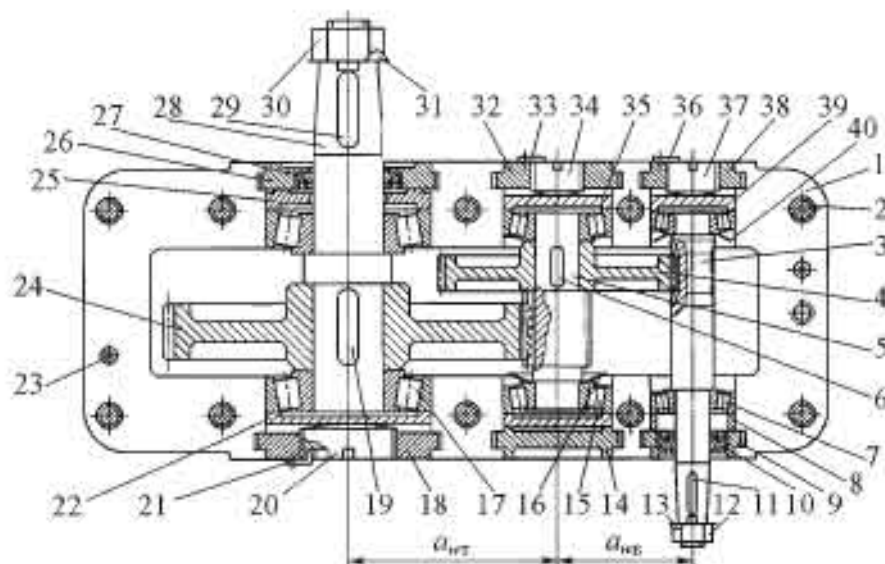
Конструкция двухступенчатого цилиндрического редуктора
